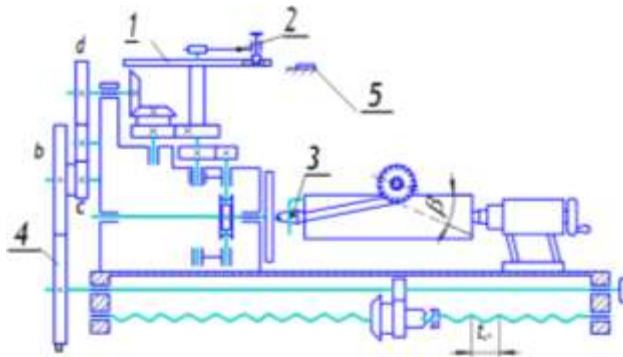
Кінематична схема налагодження ділильної головки на фрезерування гвинтової канавки
